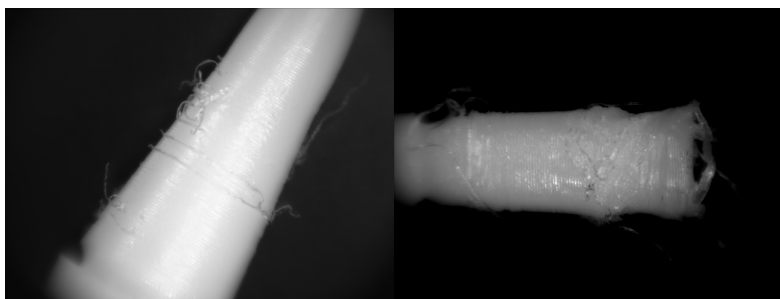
Defeitos de usinagem dos corpos de prova de UHMWPE.
